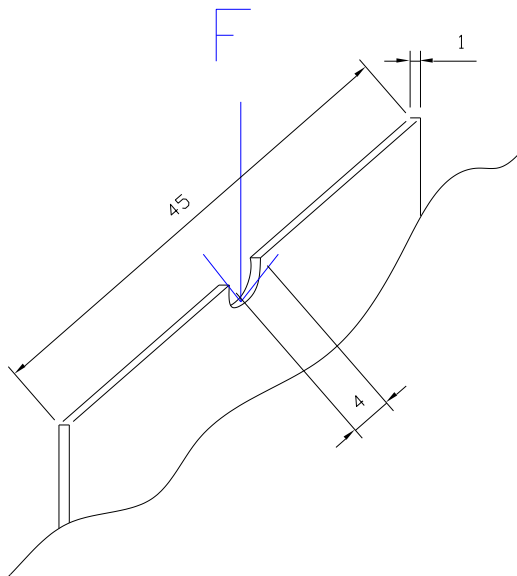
Lámina acero inoxidable sometida a esfuerzo de aplastamiento
